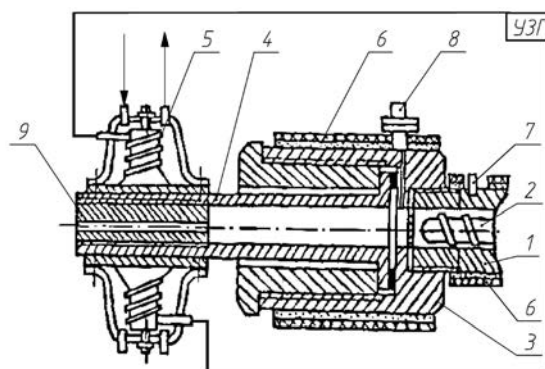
Формующий узел: 1 – материалный цилиндр экструдера; 2 – червяк; 3 – присоединительная головка; 4 – формующая головка; 5 – магнитострикционные излучатели; 6 – термозлементы; 7 – термометры; 8 – манометр; 9 – сменный канал
